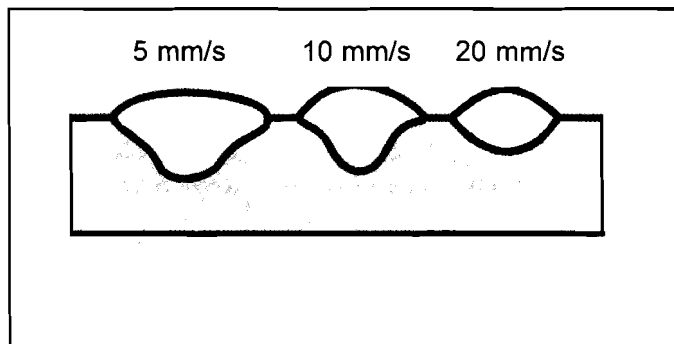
EFECTO DE LA VELOCIDAD DE SOLDEO SOBRE EL ASPECTO DEL CORDÓN EN PROCESO SEMIAUTOMÁTICO
